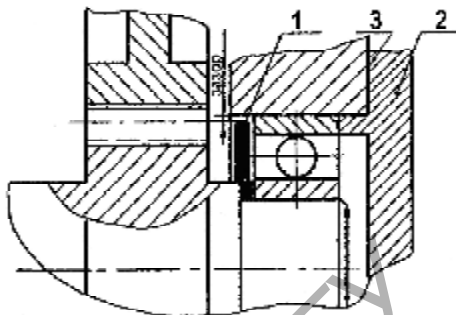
Конструкция подшипникового узла с привертной крышкой
